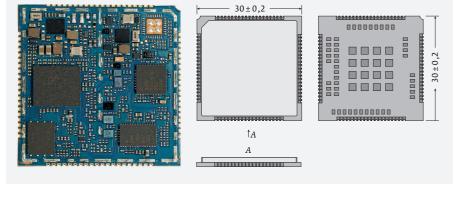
Внешний вид и размеры модуля ПР1603НБ
